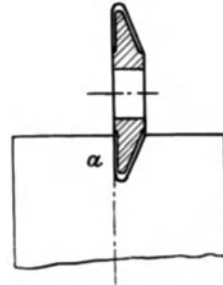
Das Fräsen der Nuten für hinterdrehte Stirnzähne.
